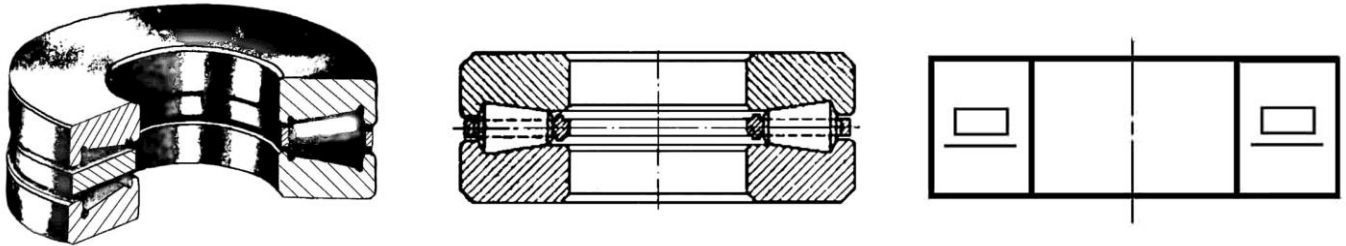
Підшипники роликові упорні типу 9000
